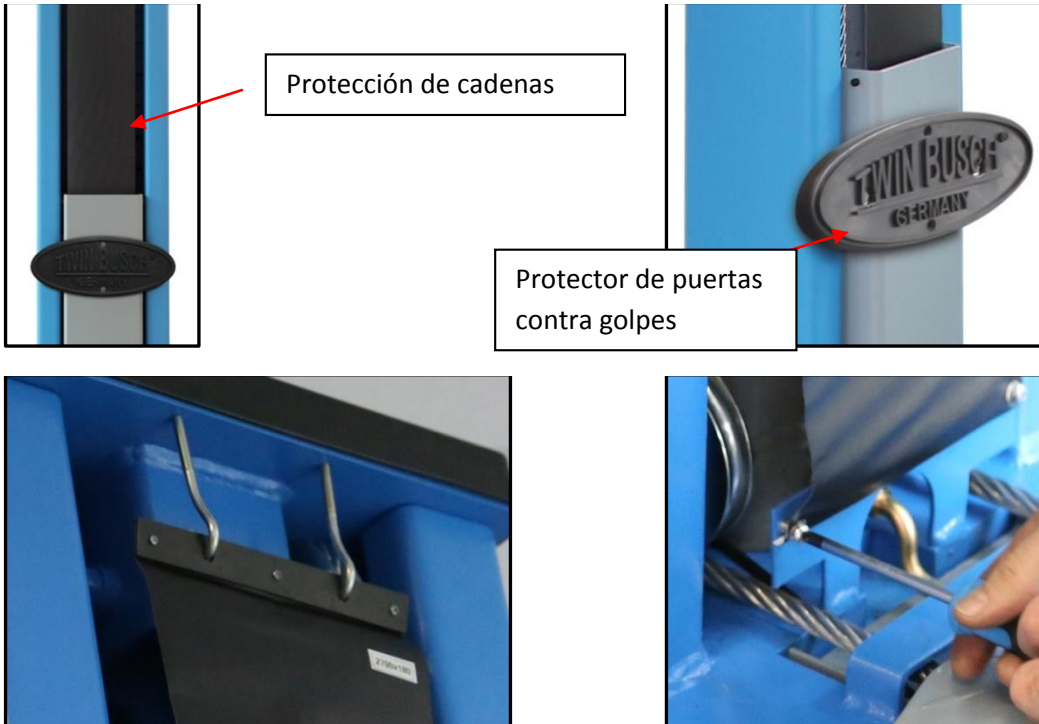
Montaje de las protecciones de cadenas y de puertas
